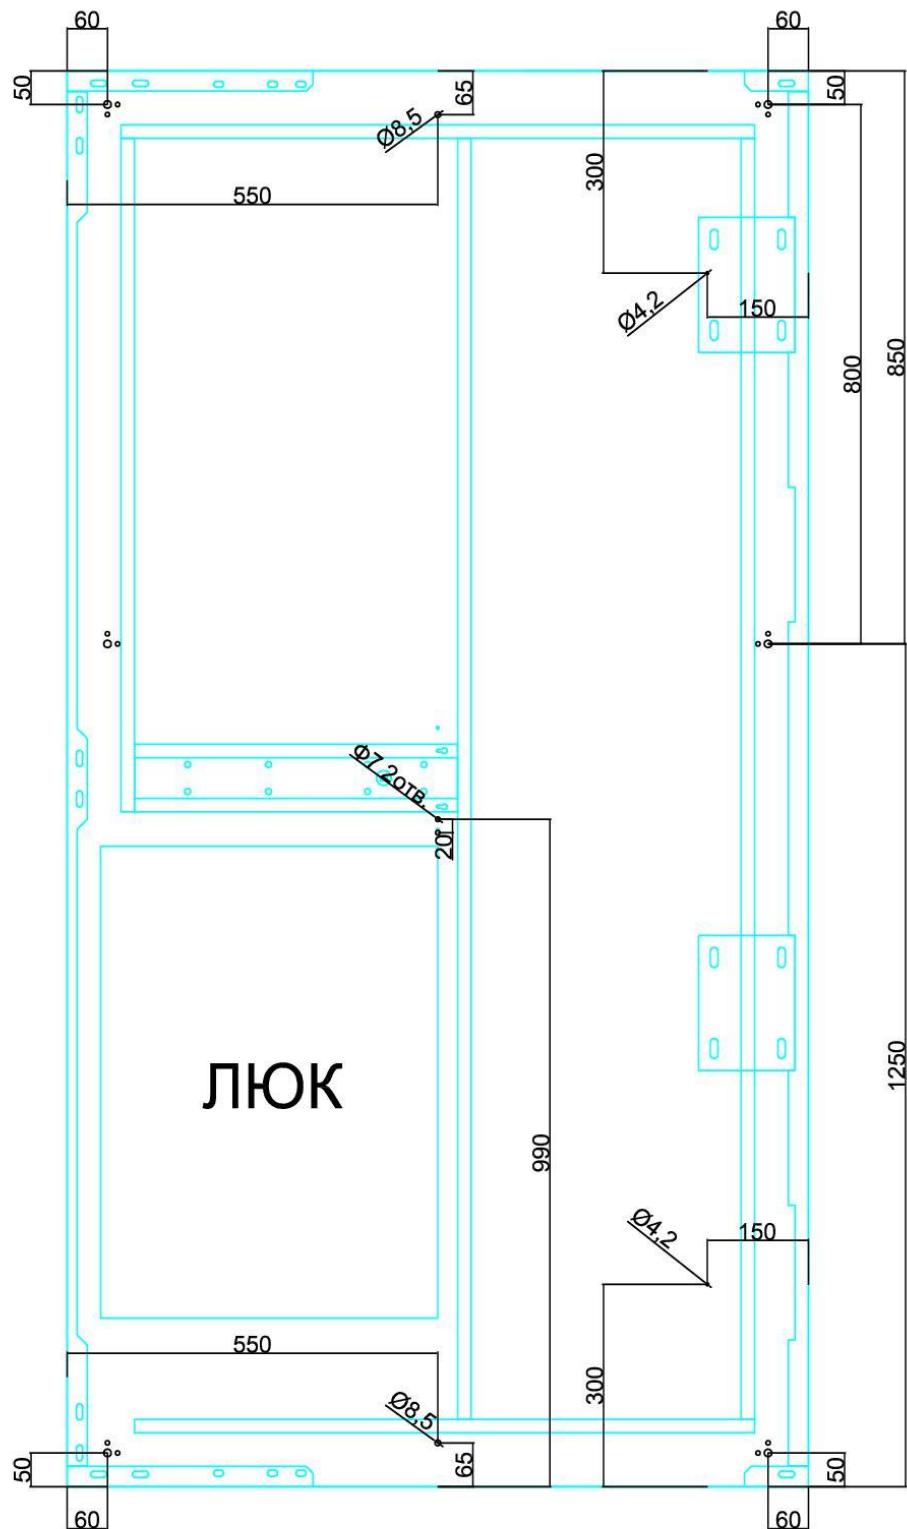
«Разметка и сверление отверстий под ввод кабеля и клемму заземления 1000 кг»
